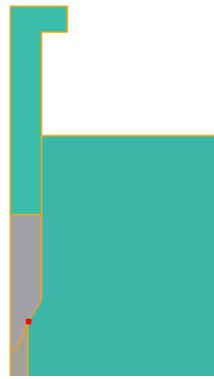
Формоутворення біметалевої заготовки , комбінація Магній-М1
